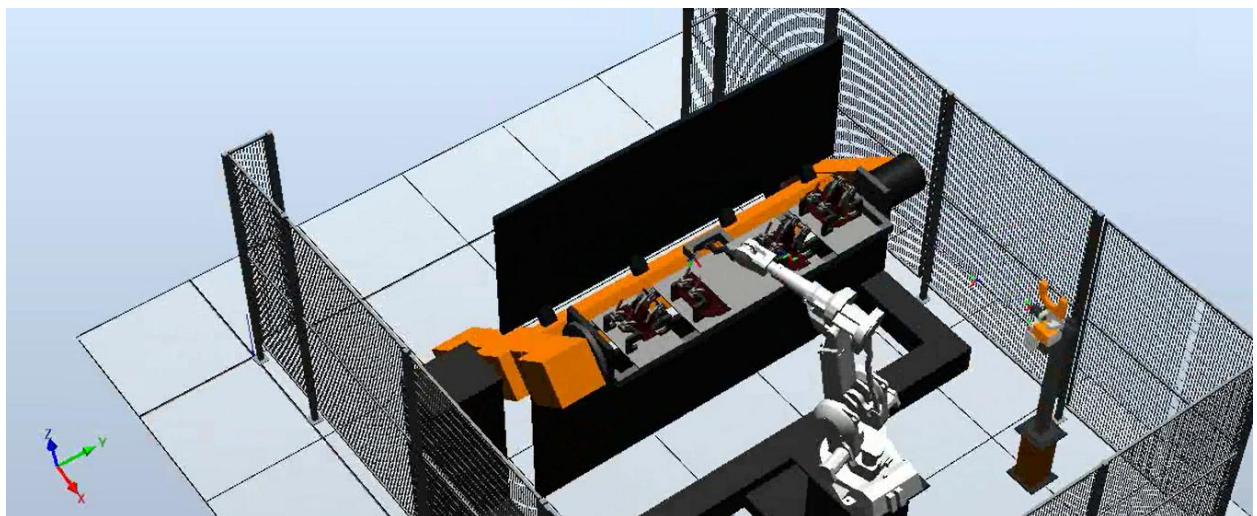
Mesa de trabajo en posición de soldadura.
